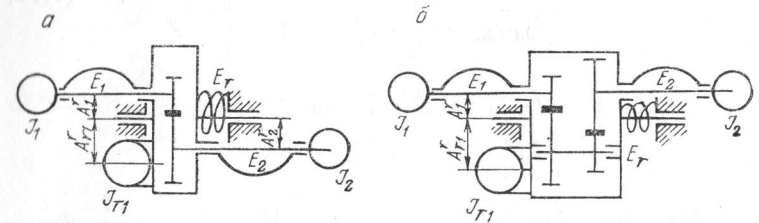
Динамические схемы коробок передач (редукторов): а — с несоосными; б — с соосными входным и выходным валами
